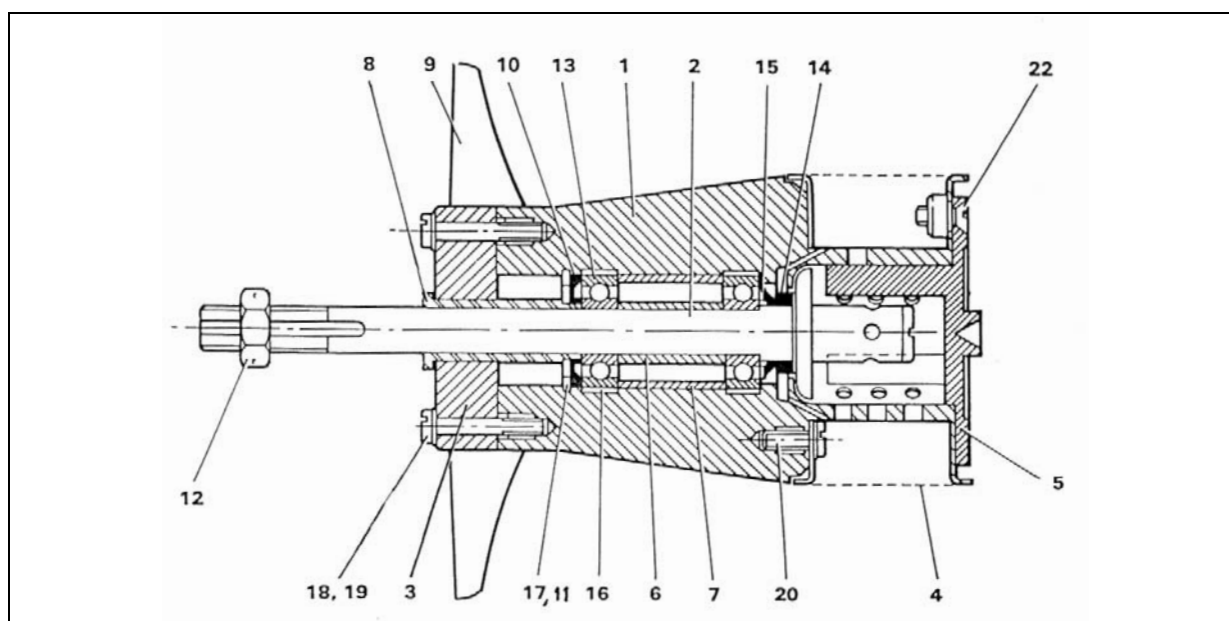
AU8115MS pièces composantes de l'atomiseur
